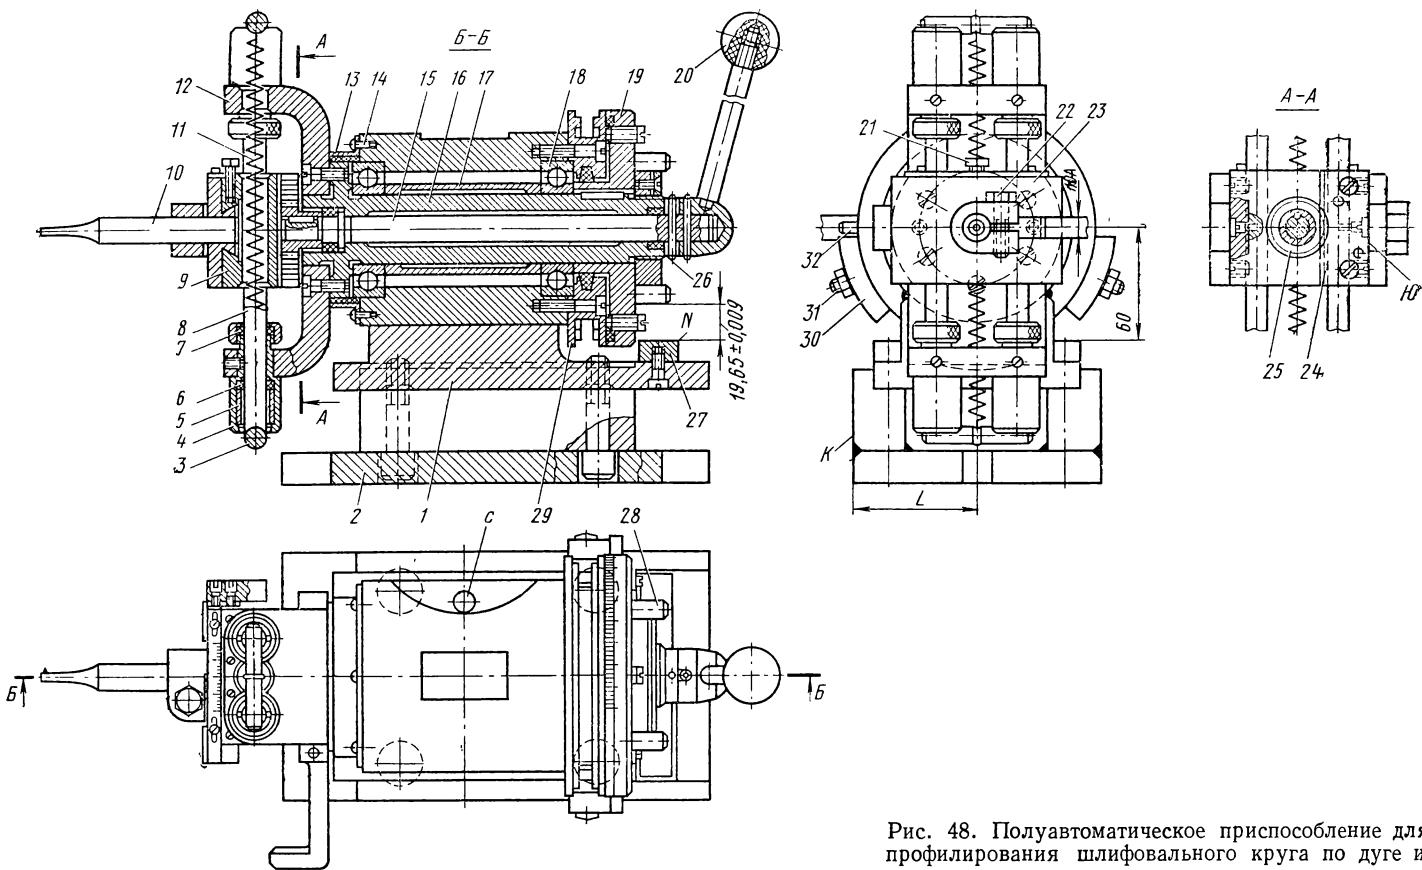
Полуавтоматическое приспособление для профилирования шлифовального круга по дуге и касательным прямым
